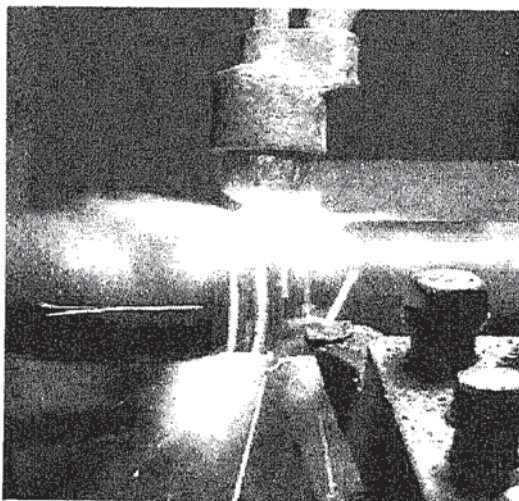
Фотография резания с нагревом цилиндрической заготовки из стали 45
